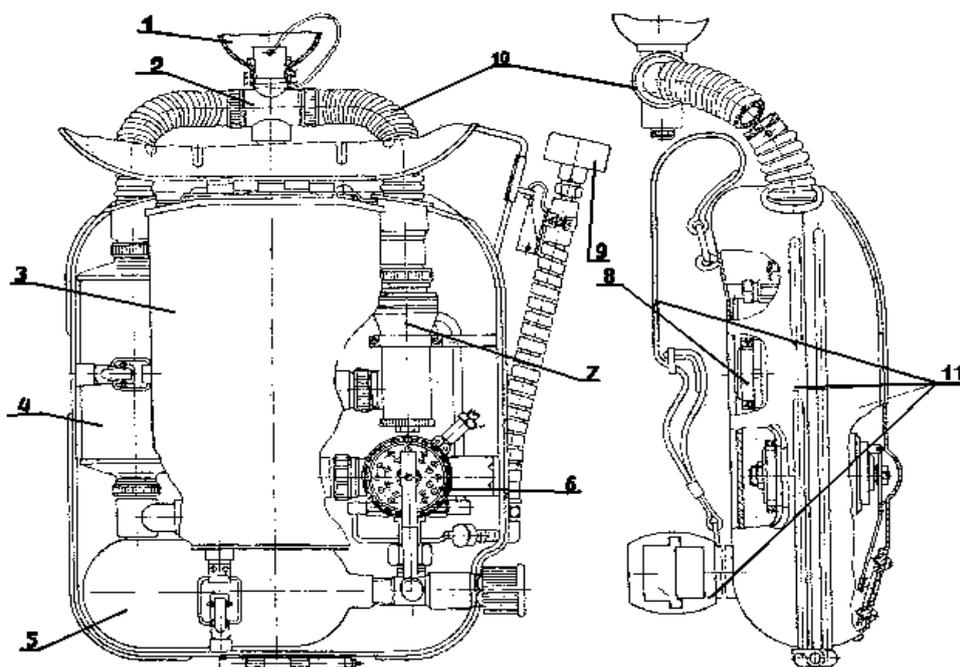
Общая схема КИП-8: 1 – шлем-маска, 2 – клапанная коробка, 3 – дыхательный мешок, 4 – регенеративный патрон, 5 – кислородный баллон с вентилем, 6 – блок легочного автомата и редуктора, 7 – звуковой сигнал, 8 – предохранительный клапан дыхательного мешка, 9 – манометр выносной, 10 – гофрированные трубки, 11 – корпус с крышкой и ремнями
